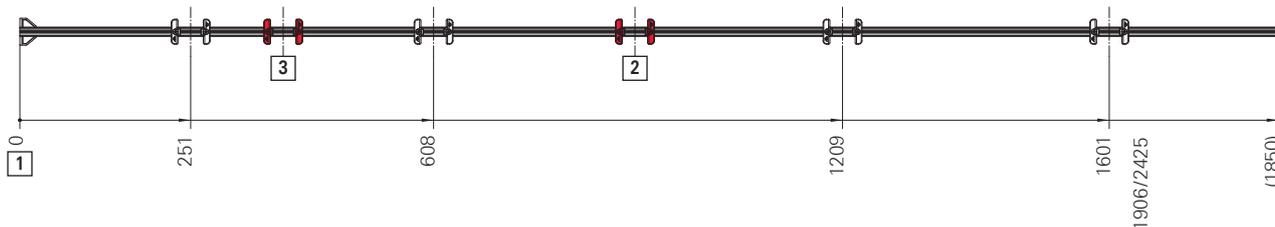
[1] tope perfil de deslizamiento; [2] posición de adaptador para bulón de cierre 1906; [3] posición de adaptador para bulón de cierre 2425
